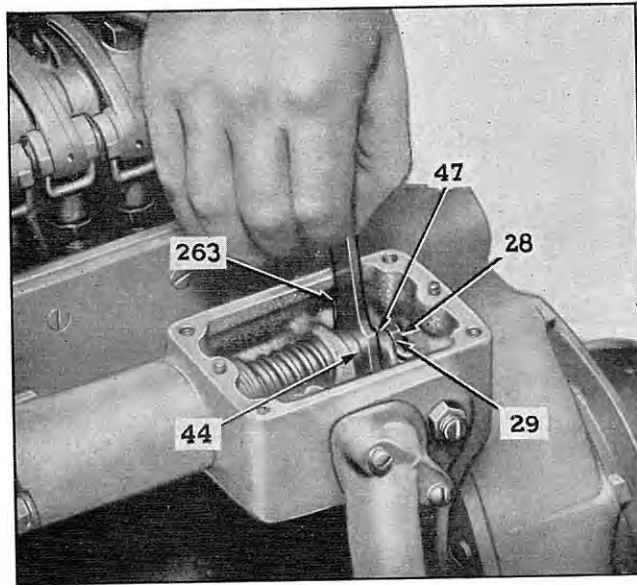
Réglage du jeu du régulateur (SW-LS)
